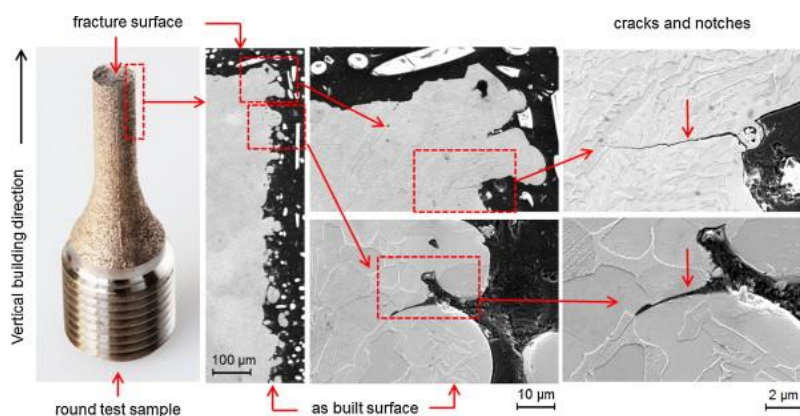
Illustration des départs de fissures depuis la surface irrégulière brute de fabrication [34].
